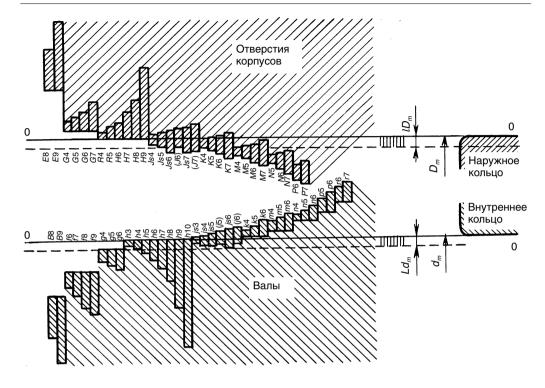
Схемы расположения полей допусков для посадок подшипников качения на вал и в корпус
